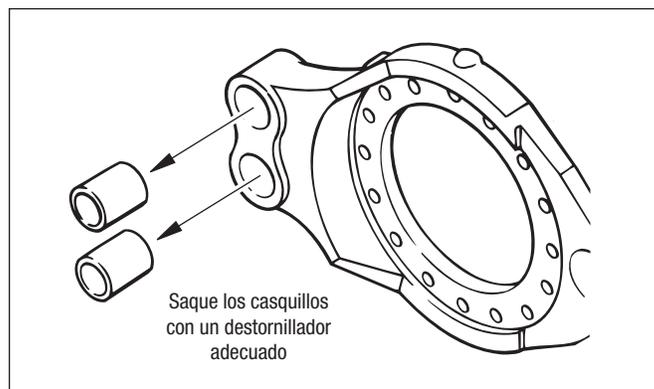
Desmontaje de casquillo de pasador de anclaje
